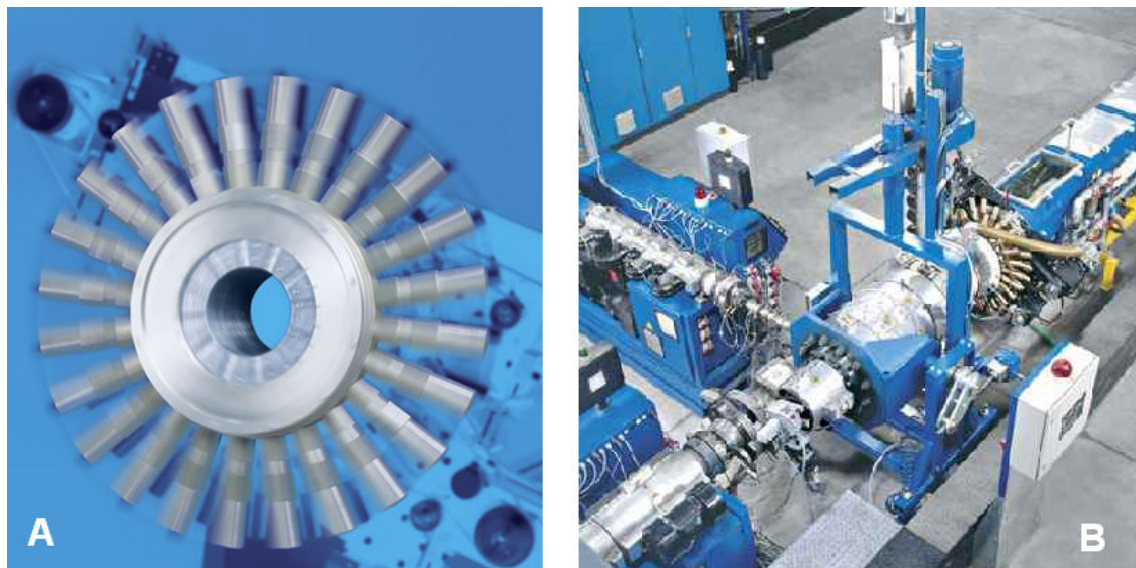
a) Sistema de cambio rápido de diámetro de tubería; b) Vista de planta de la unidad de procesamiento Quick Switch de Krauss Maffei que actualmente se encuentra montada en Egeplast.
